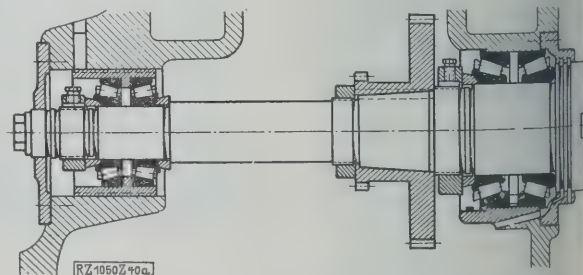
Spindellagerung einer amerikanischen Fräsmaschine in Doppel-Schrägrollenlagern.
